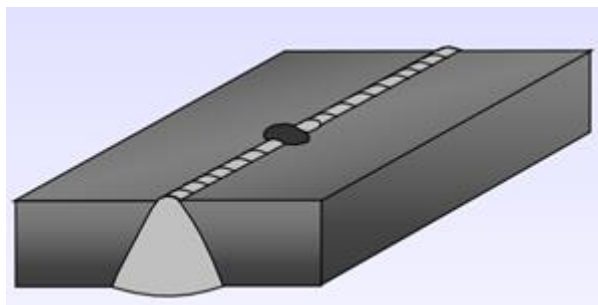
Gaurire. Sursă: M.S. Rogers, Welding Inspection Defects/Repairs Course Reference WIS 5, 2003.
